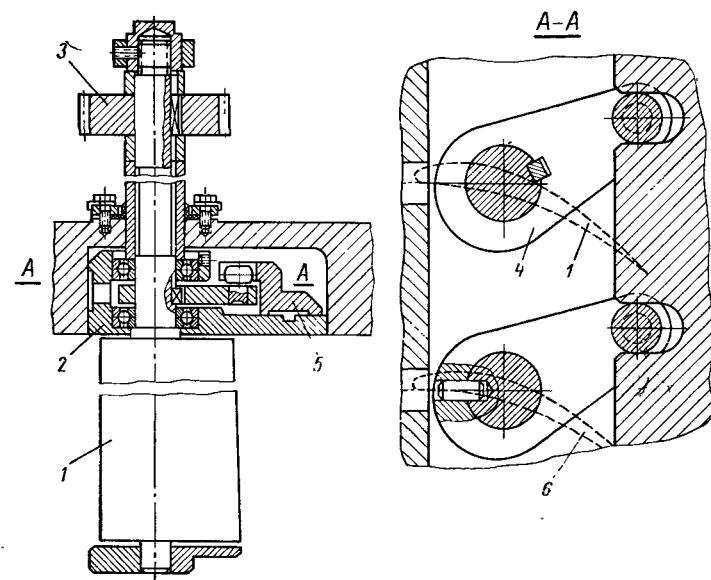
Поворотный направляющий аппарат компрессора ГТУ мощностью 50 000 квт:
